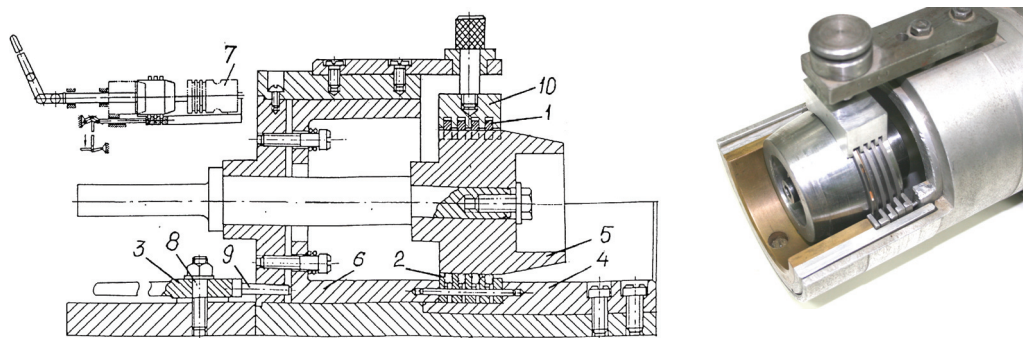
Приспособление для одновременной сборки поршневых колец: схема и фотография колец, разжатых конусной оправкой
